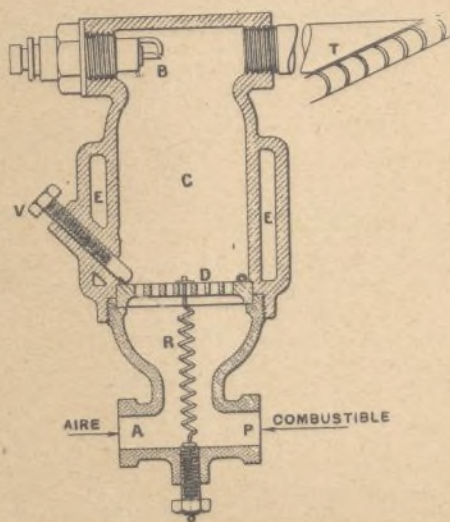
Cámara de combustión de la turbina Karavodine.
